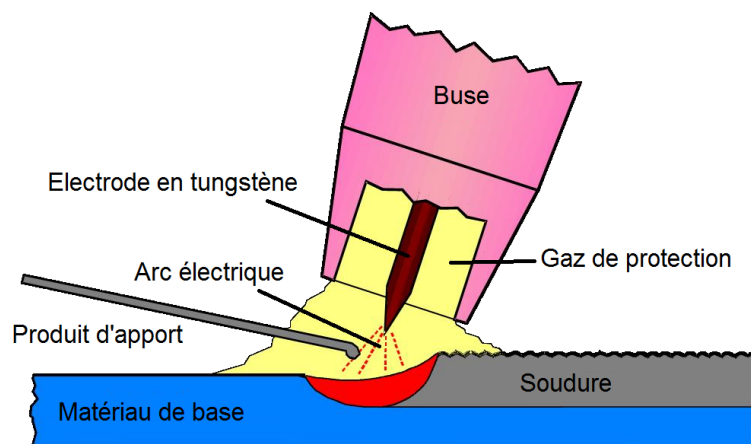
Soudage TIG (Institut de soudure 2021c)
